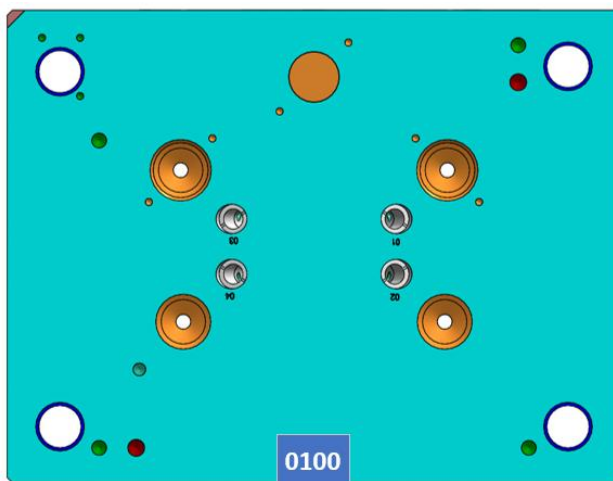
Placa moldante, lado da injeção em vista de baixo
